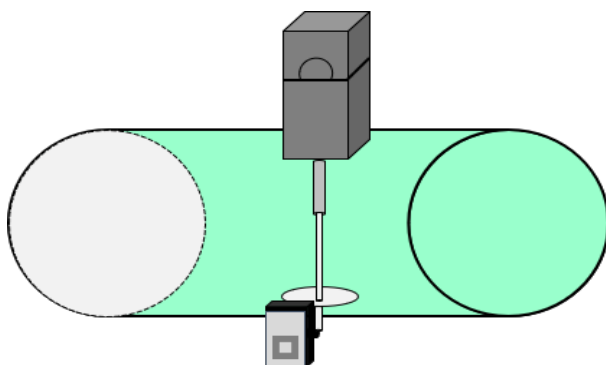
Diseño de ensayo para la medición de la temperatura durante la soldadura
